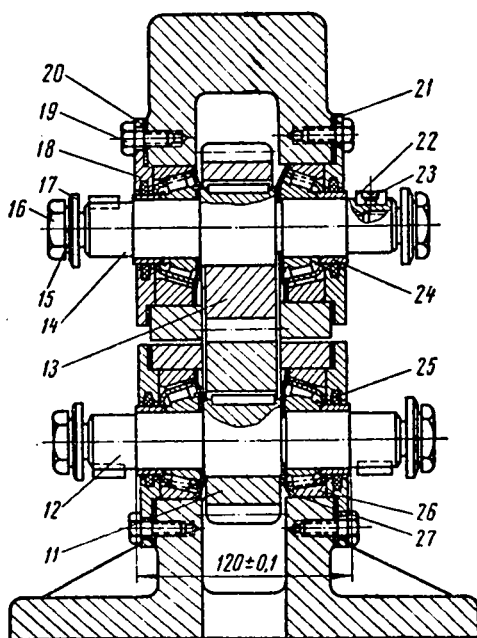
Рабочий механизм станка ФП-2 (а) (см. рис. 245, б)
